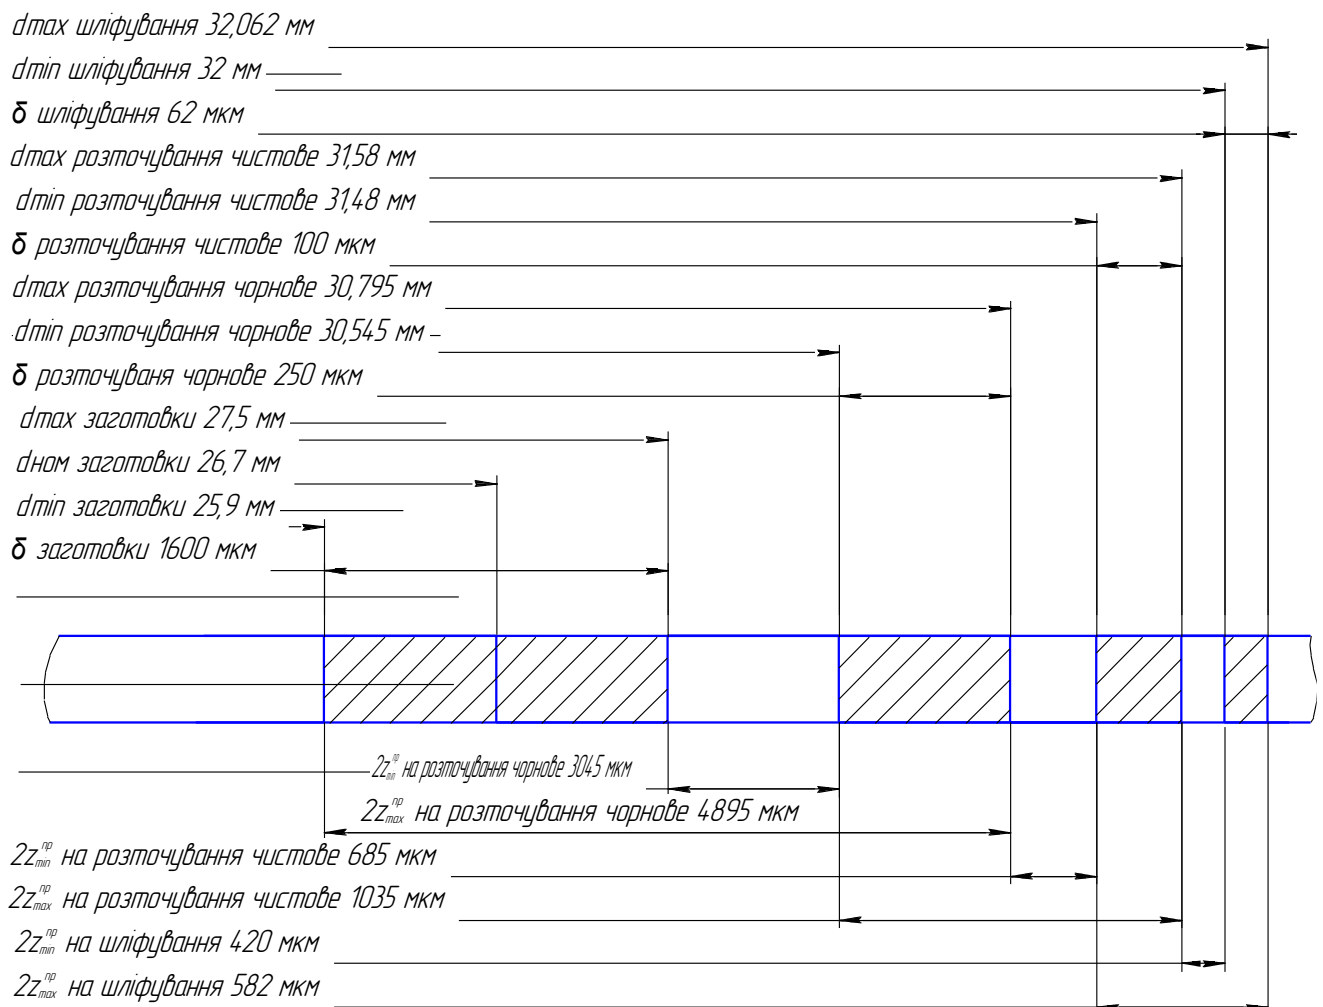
Схема розташування припусків та допусків
